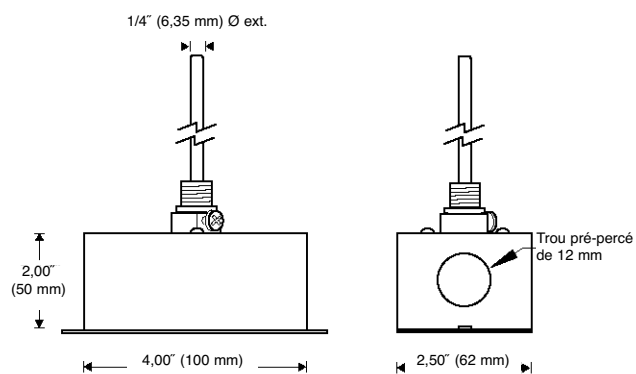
Les dimensions de la sonde de température TE-703 C/D sont exprimées en pouces et en millimètres (mm).
